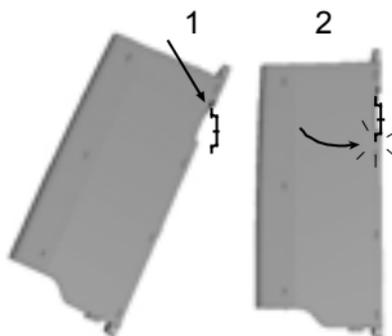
Montagem com trilho DIN, MI1 - MI3
